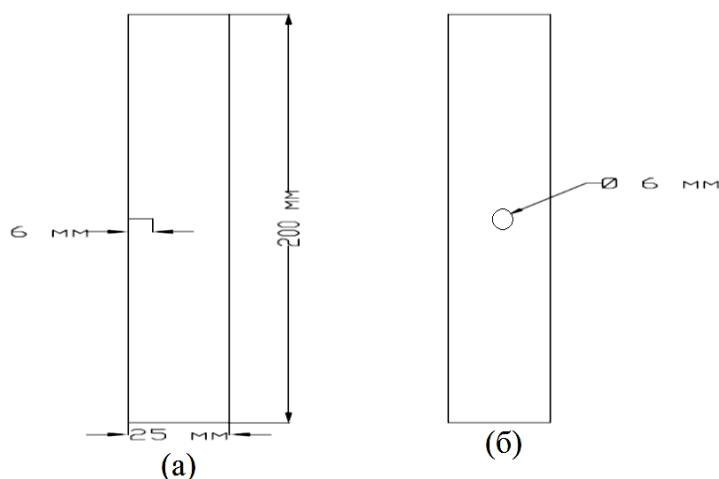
Схема образцов с дефектами «боковая прорезь» (а) и «отверстие»(б)
